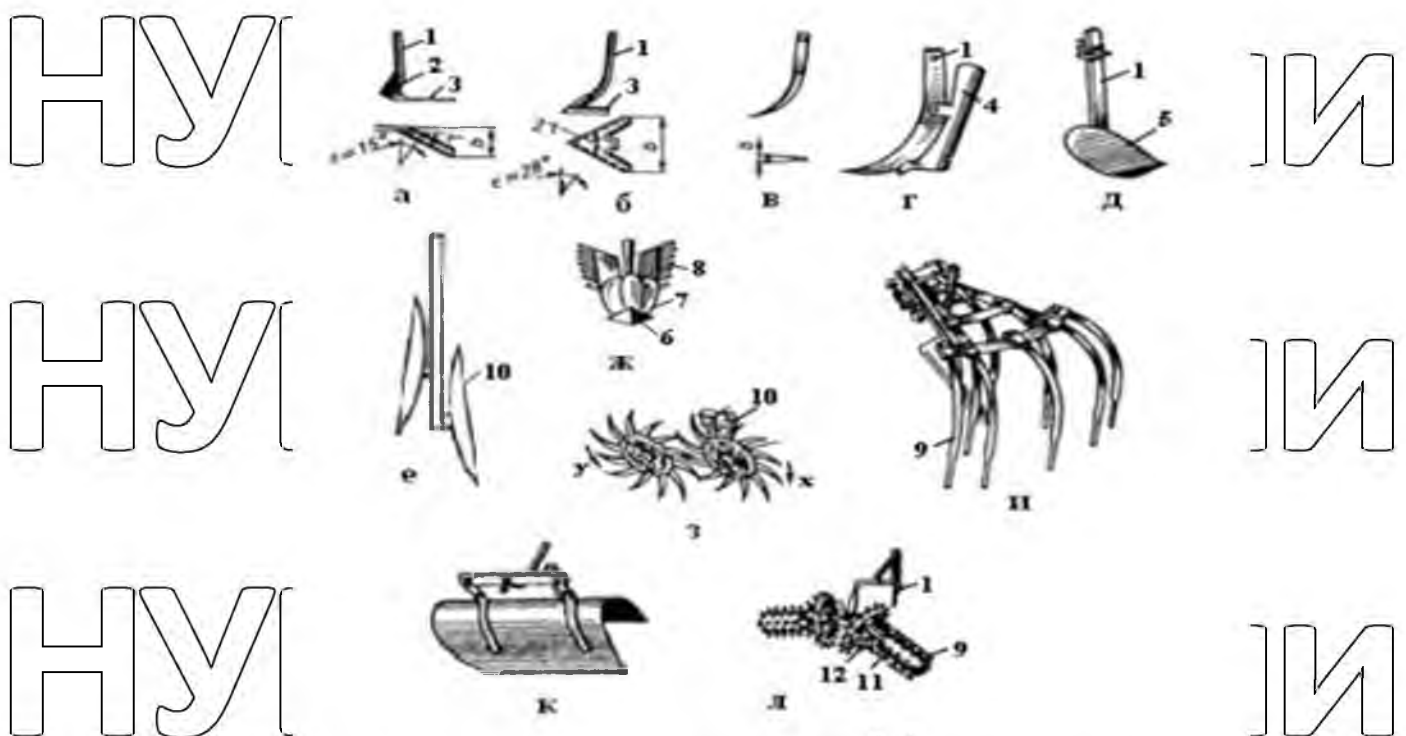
Робочі органи просапних культиваторів: а - одностороння плоскоріжуча лапа-бритва; б - універсальна стрілчаста лапа; в - долотоподібна розпушувальна лапа; г - підгодівельний ніж; д - лапа-відвальчик; е - підсапувальні диски; ж - підсапувальний корпус; з - голчасті диски; и - просапні боронки; к - щиток-будиночок; л - універсальні ротаційні боронки; 1 - стійка; 2 - щока; 3 - лезо; 4 - лійка; 5 - відвальник; 6 - норальник; 7 - відвал; 8 - крило відвалу; 9 - зуби; 10 - диски; 11 - циліндричний барабан; 12 - конічний барабан.
